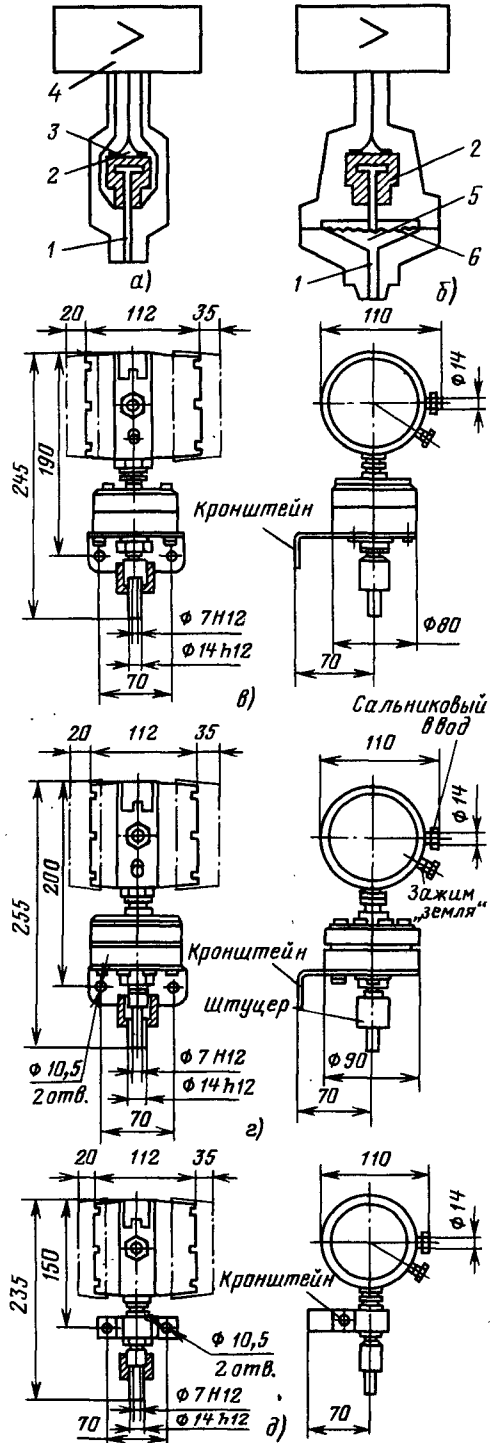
Схема устройства, габаритные, присоединительные и установочные размеры тензометрических преобразователей давления серии «Сапфир-22»:
